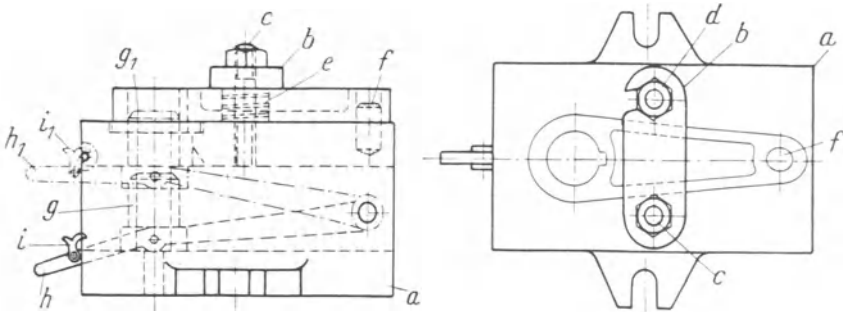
Nuten-Stoßvorrichtung für Hebelnaben.
